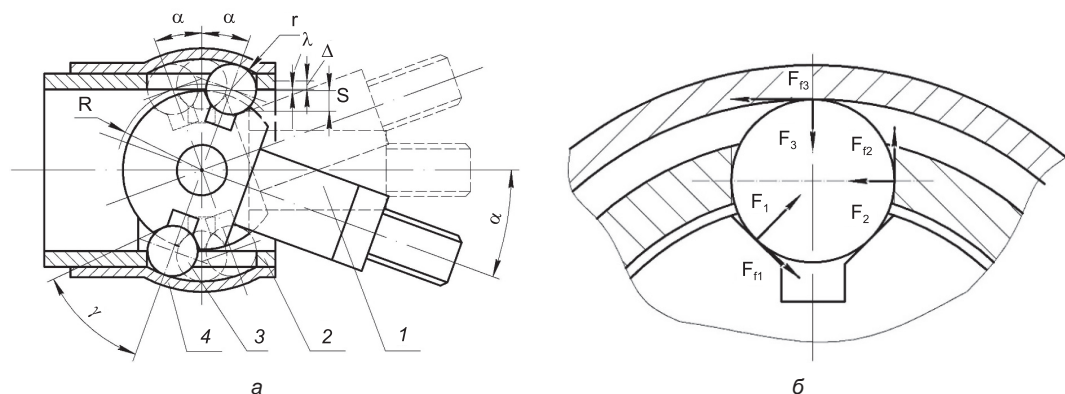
Конструктивна схема шарнірного з'єднання (а) секцій гвинтового робочого органу та розрахункова схема (б) для визначення силових параметрів, що діють на кульку під час передачі обертового моменту: 1 — сферичний палець; 2 — циліндрична втулка; 3 — кулька; 4 — втулка зі сферичною поверхнею
